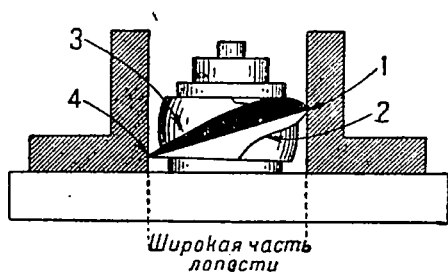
Приспособление для проверки шага винта: 1—ребро атаки; 2—рабочая сторона лопасти; 3—верхняя часть лопасти; 4—ребро обтекания.
